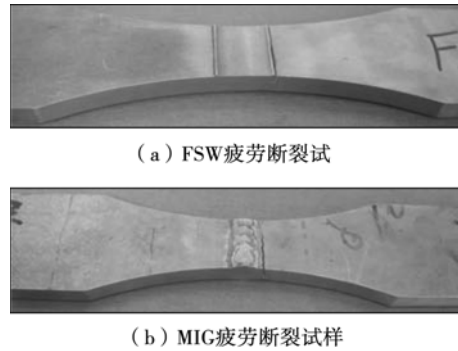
6082 铝合金 FSW 及 MIG 焊疲劳断裂试样
